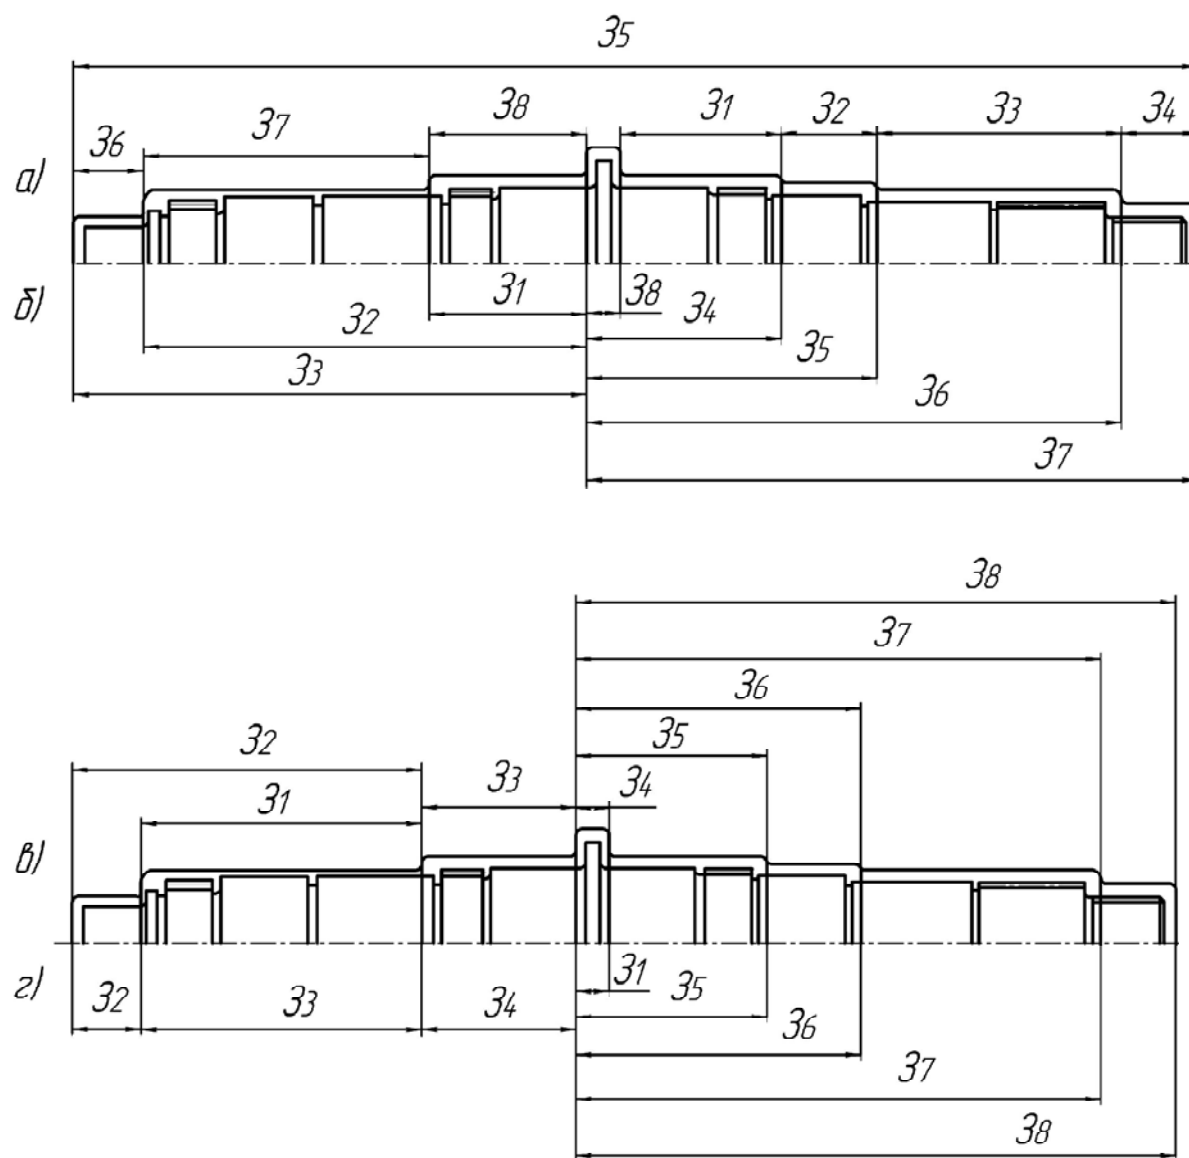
Эскиз заготовки вала первичного с вариантами простановки линейных размеров:
